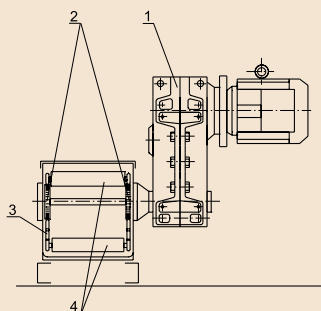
Привод цепного конвейера на базе вертикального редуктора:
